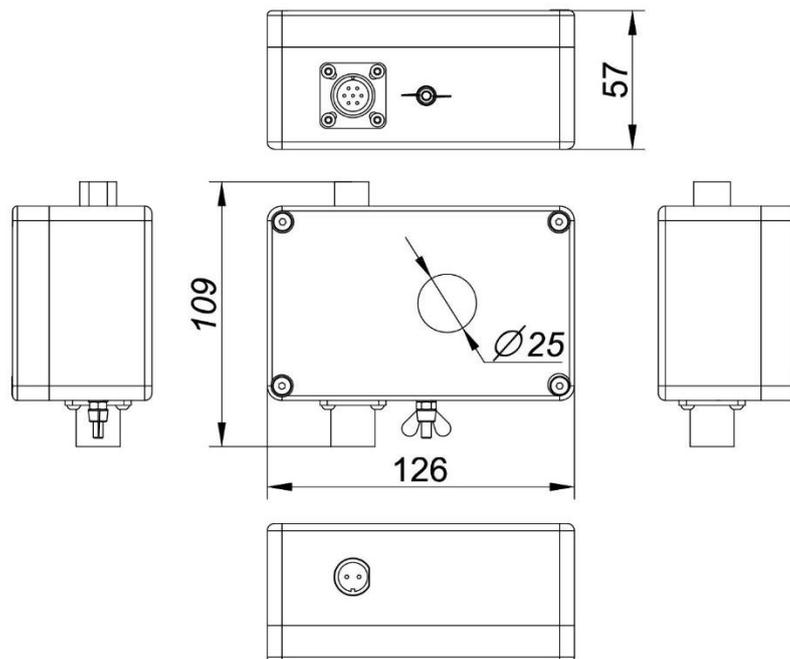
Габаритные размеры выносного датчика тока и напряжения ИРСП11-Д-500А
